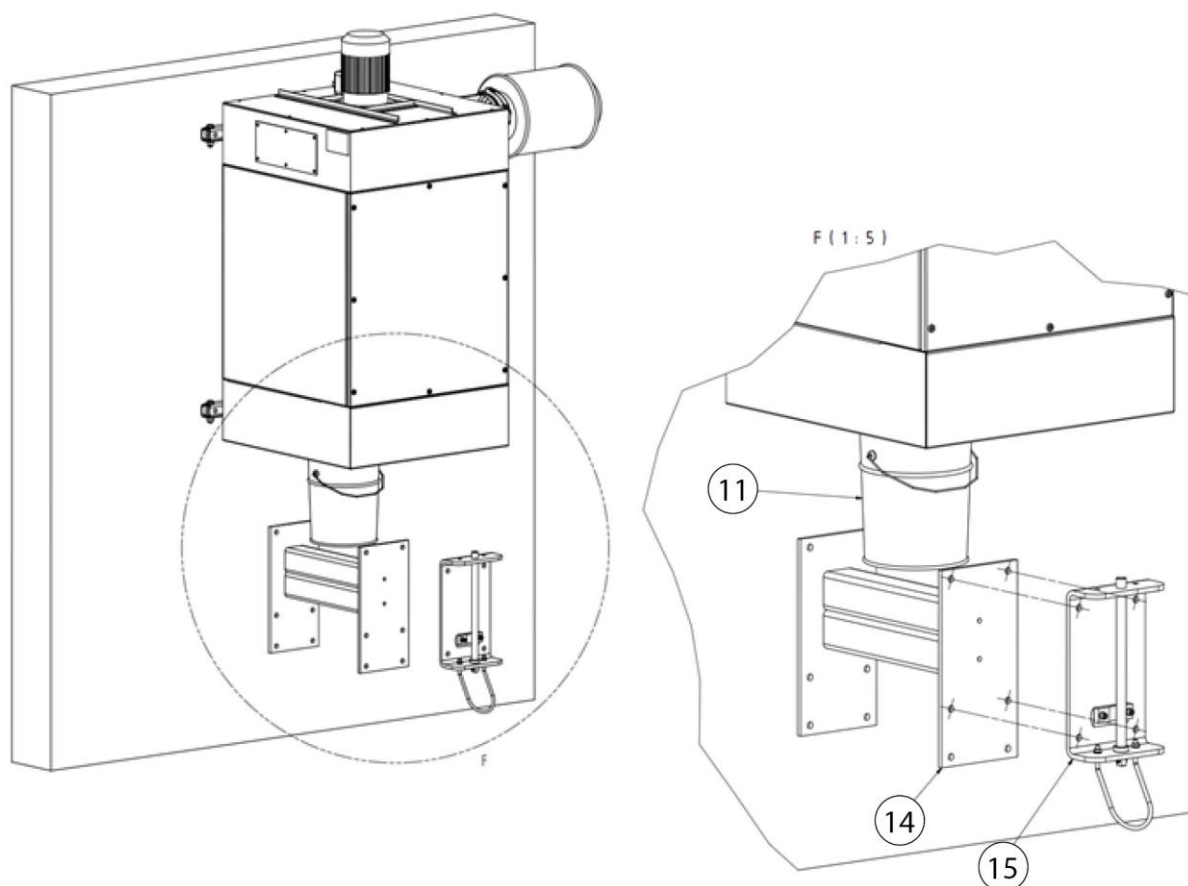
Montagem do braço de aspiração de 5 – 10m
